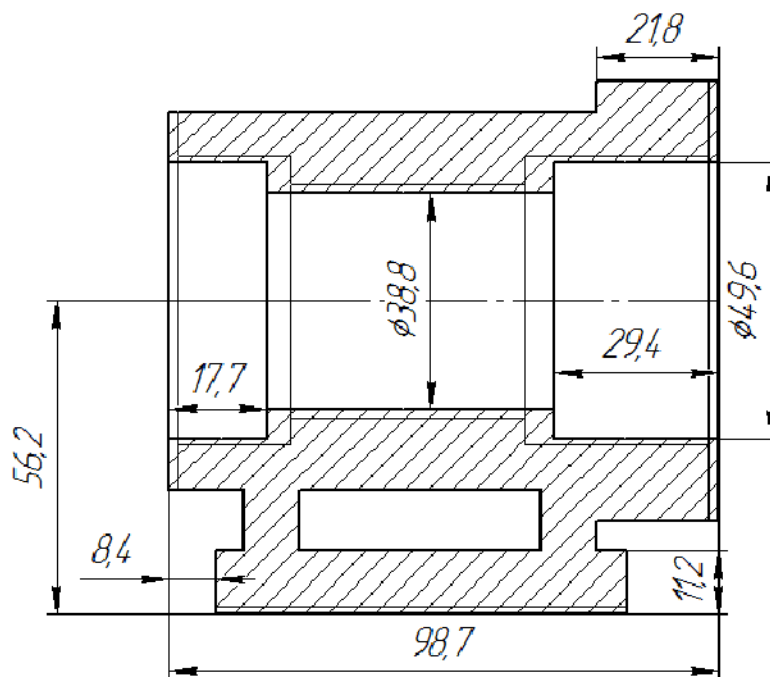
Ескіз заготовки при литті в піщано-глинисті форми
